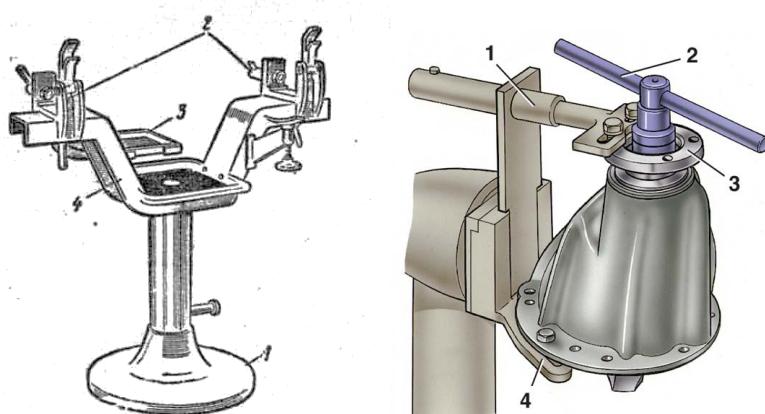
Стенды для ремонта мостов и редукторов автомобилей
